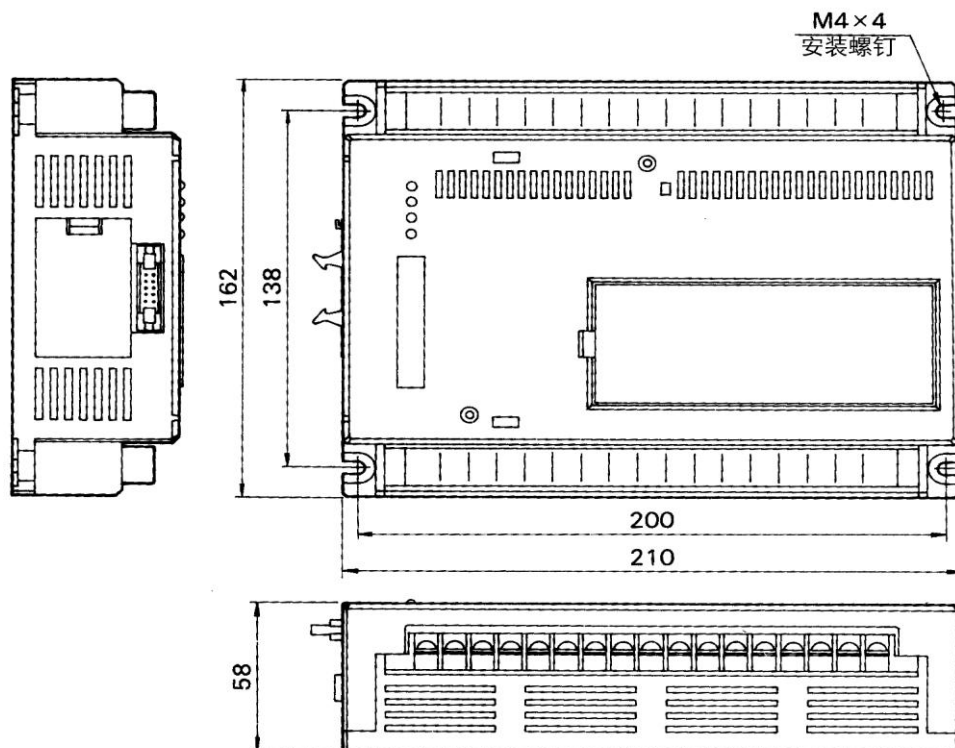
SE-11 PC 基本单元外形尺寸图 (单位: mm)
